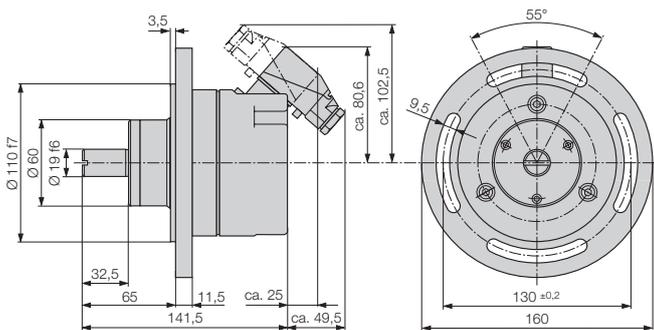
KINAX WT 707 mit Steckverbinder und Flansch.
